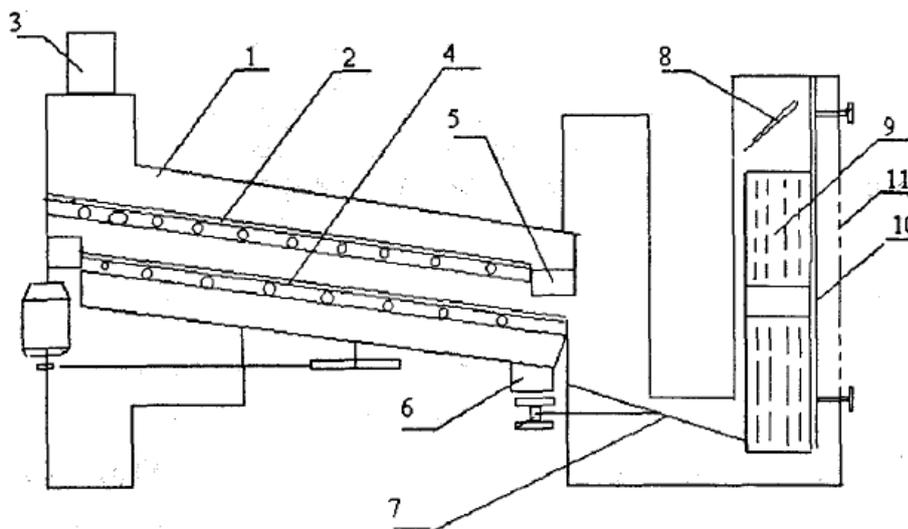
Схема сепаратора А1-БИС-100: 1 – корпус; 2 – сортировочное сито; 3 – патрубок; 4 – подсевное сито; 5, 6 – лоток; 7 – питатель; 8 – регулятор; 9 – пневмоканал; 10 – подвижная стенка; 11 – жалюзи
